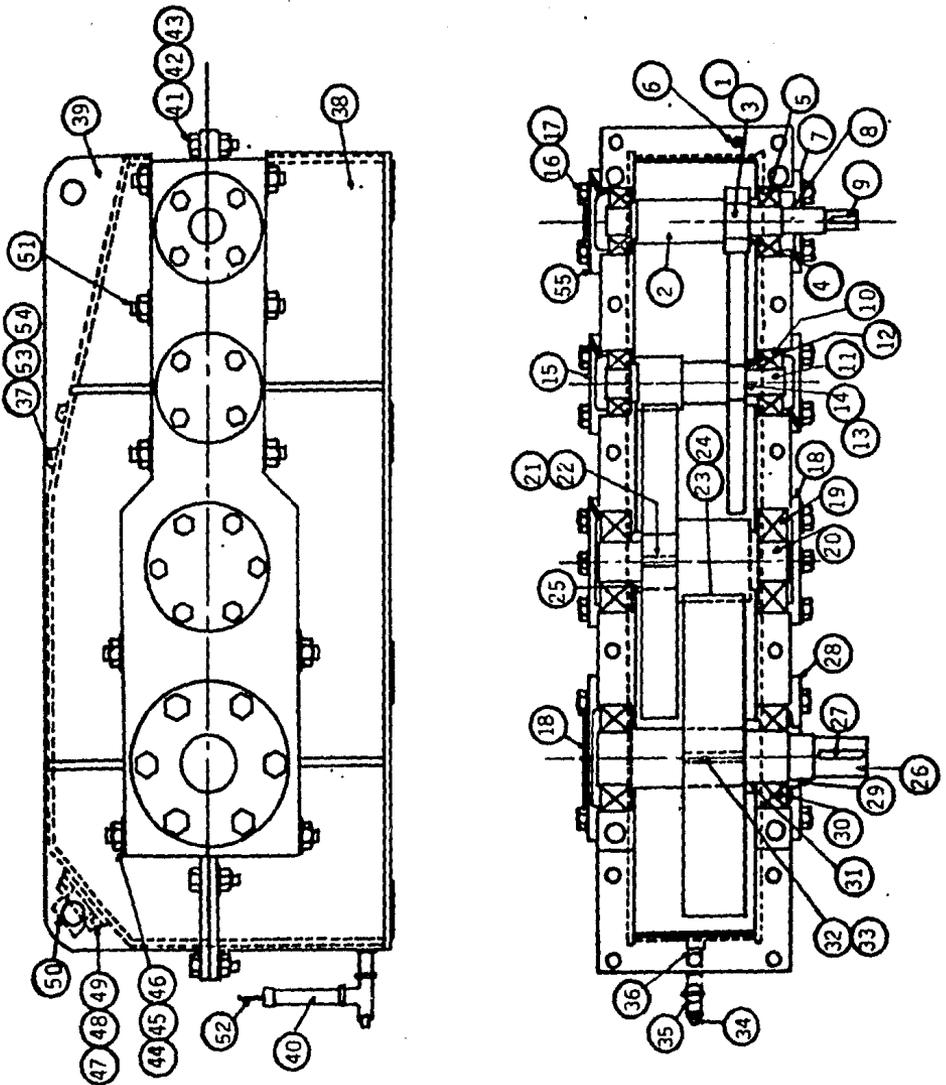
ARREGLO GENERAL DEL REDUCTOR DE IZAJE PRINCIPAL
